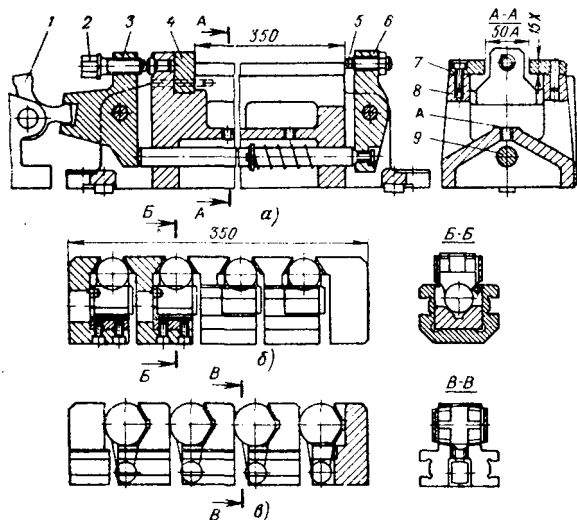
Универсально-наладочное приспособление с наладками для фрезерования плоскостей в деталях типа рычагов
